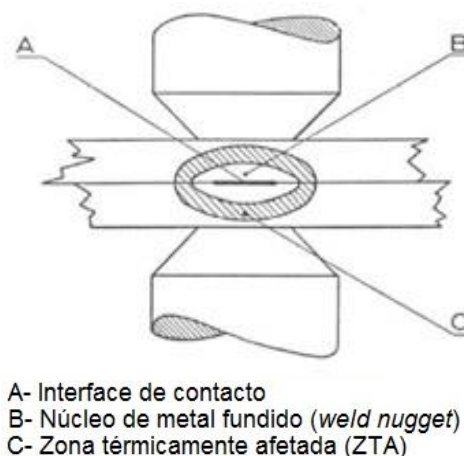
Formação do núcleo de metal fundido (*weld nugget*) na soldadura por resistência na interface chapa-chapa [31].
